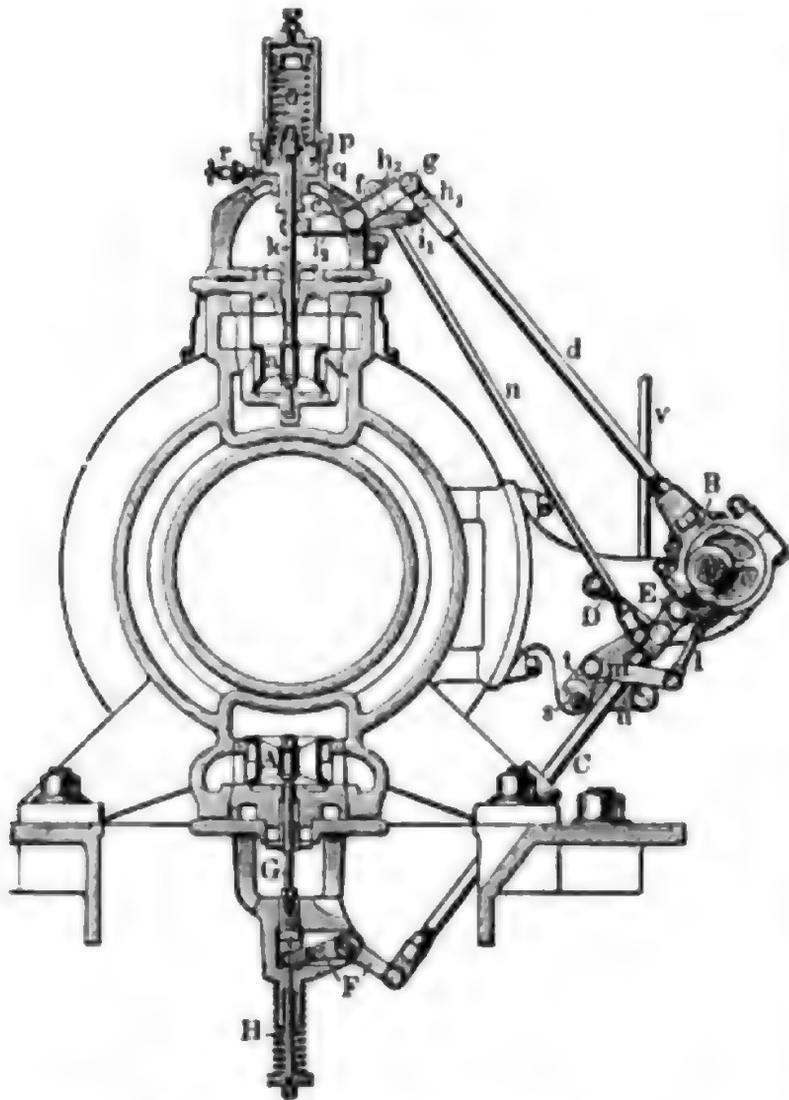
gibt ein Bild einer Ausführungsform der Sulzersteuerung für die eine Zylinderseite einer liegenden Maschine. Es ist ein Querschnitt an einem
